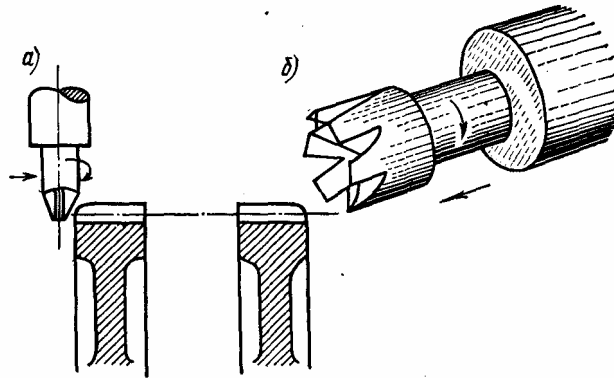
Закругление зубьев цилиндрических зубчатых колес:
